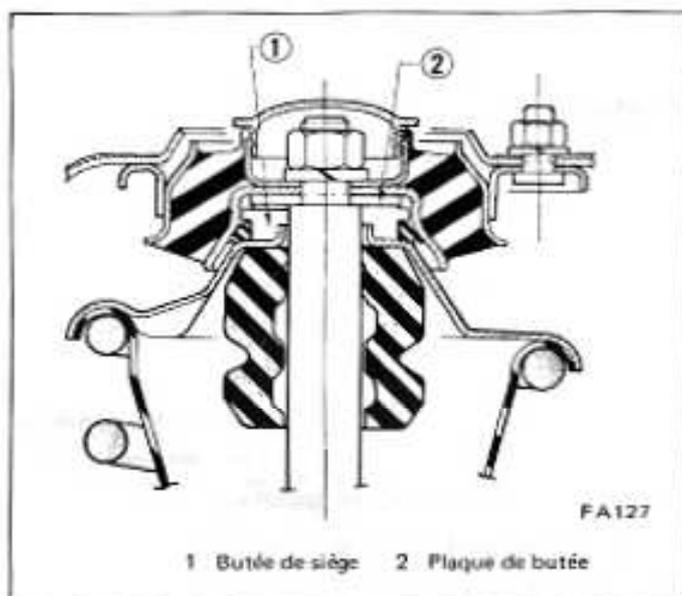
Vue en coupe de l'emplacement de butée de siège
